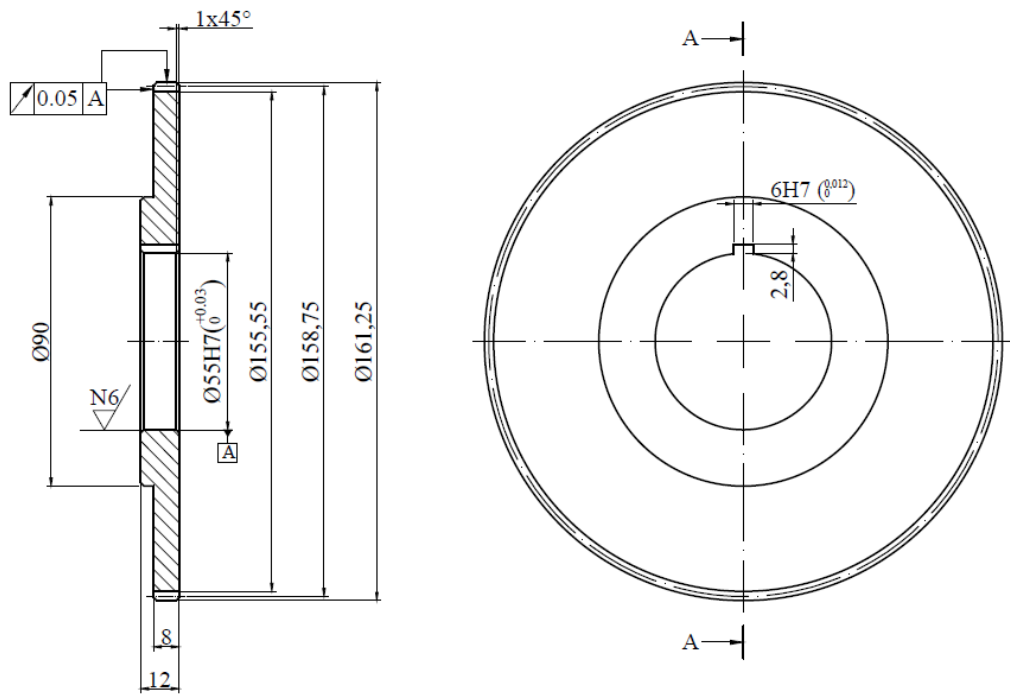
Design *change gear* untuk mesin bubut *knuth basic plus
